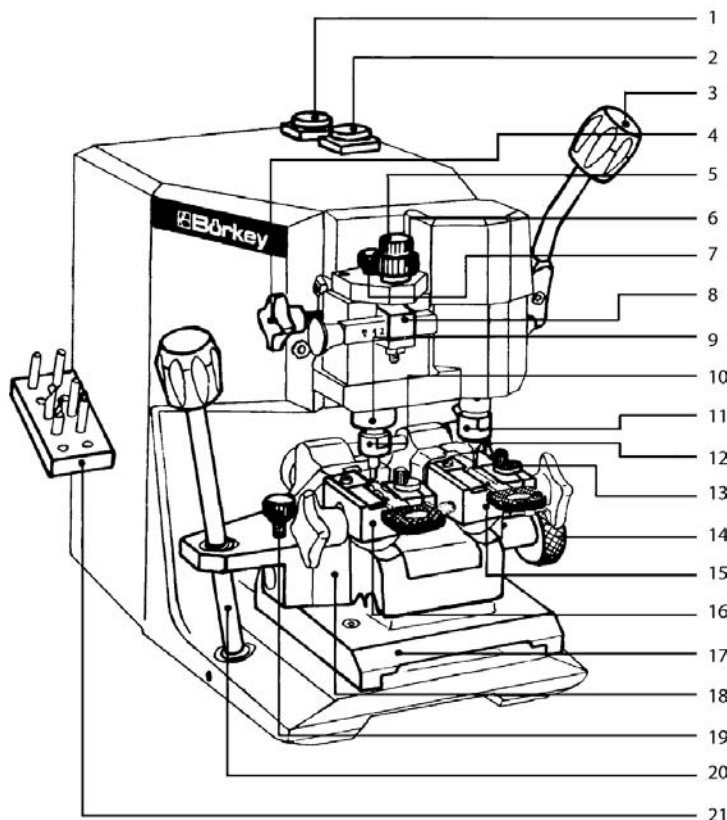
Детали станка Borkey 989 Top-Cut: 1 — выключатель подсветки;
